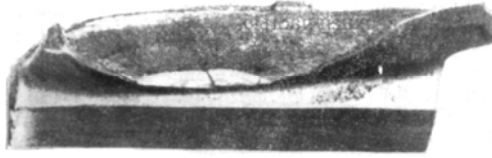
Вид втомного зламу робочої лопатки компресора
